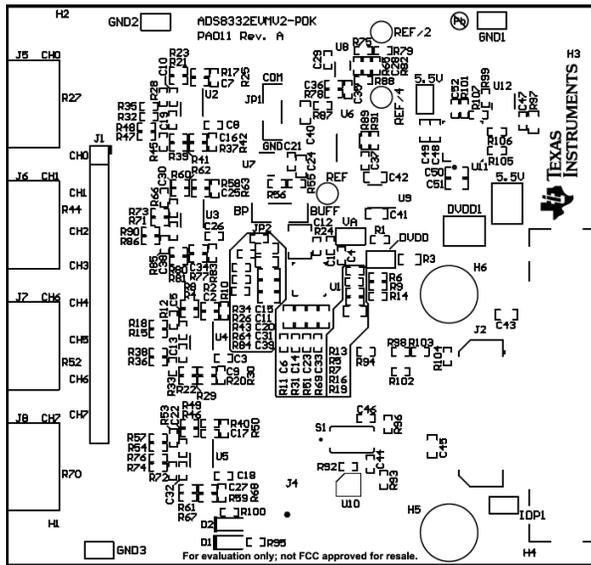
ADS8332EVMV2 PCB : 顶部覆盖层
